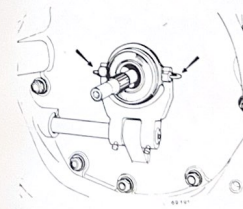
Cojinete de desembrague unido a la horquilla de mando.
